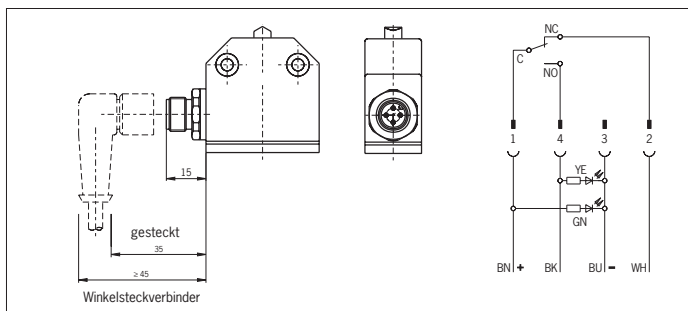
Maßzeichnung/Anschlussplan N01.550C1526 mit Steckverbinder M12 (4-polig)
